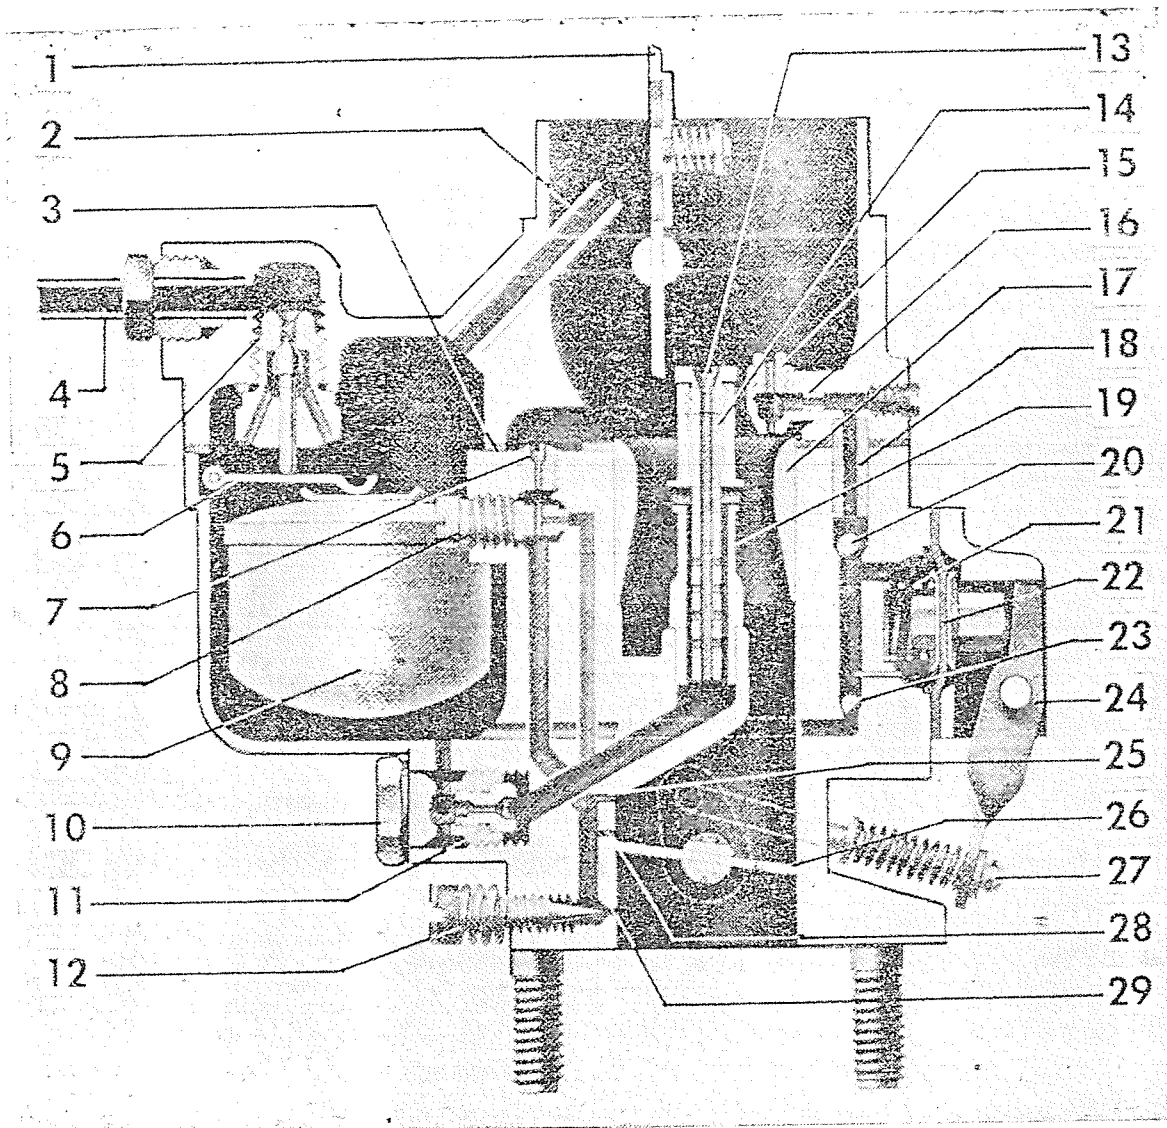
Sección transversal del nuevo carburador Solex 28 PCI con bomba incorporada.
